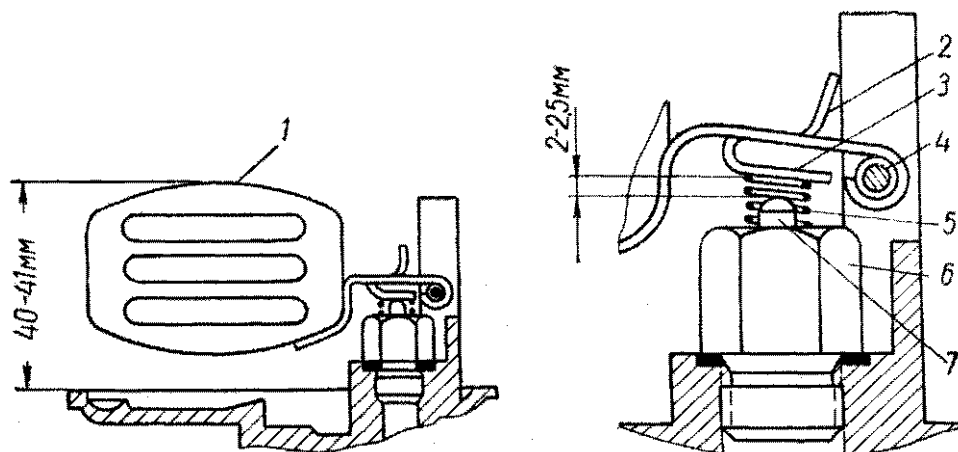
Поплавок карбюратора К-124 и его регулировка:
